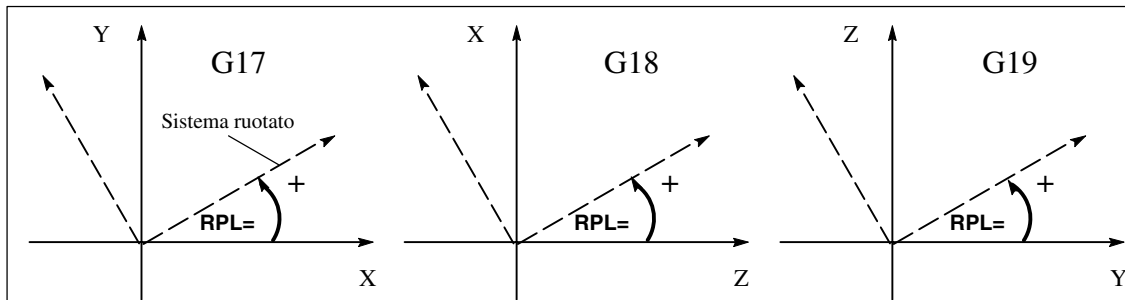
Definizione della direzione positiva dell'angolo di rotazione nei diversi piani
